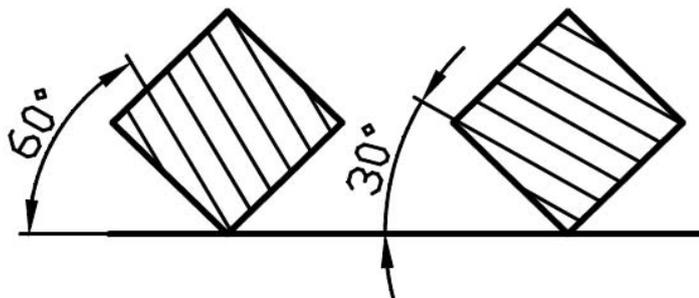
Штриховка под углом 60° и 30° к рамке чертежа
